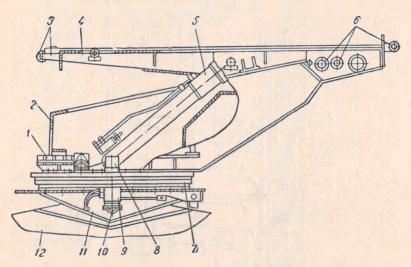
Подъемно-поворотное устройство автолестницы АЛ-45(257), ПМ-109:
